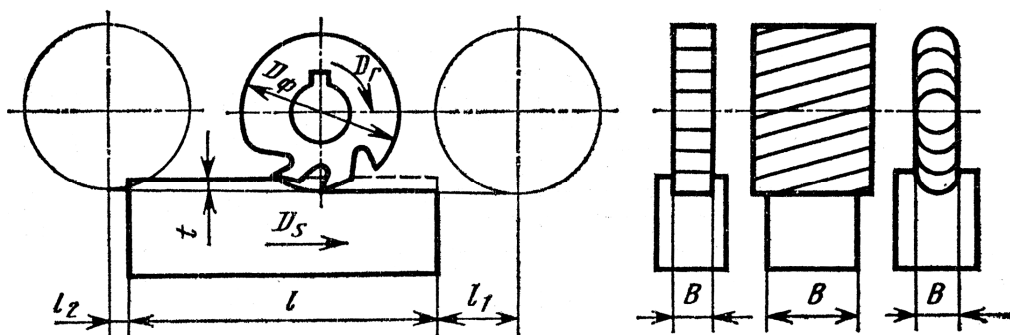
Путь, пройденный инструментом при фрезеровании фасонными, дисковыми и цилиндрическими фрезами
